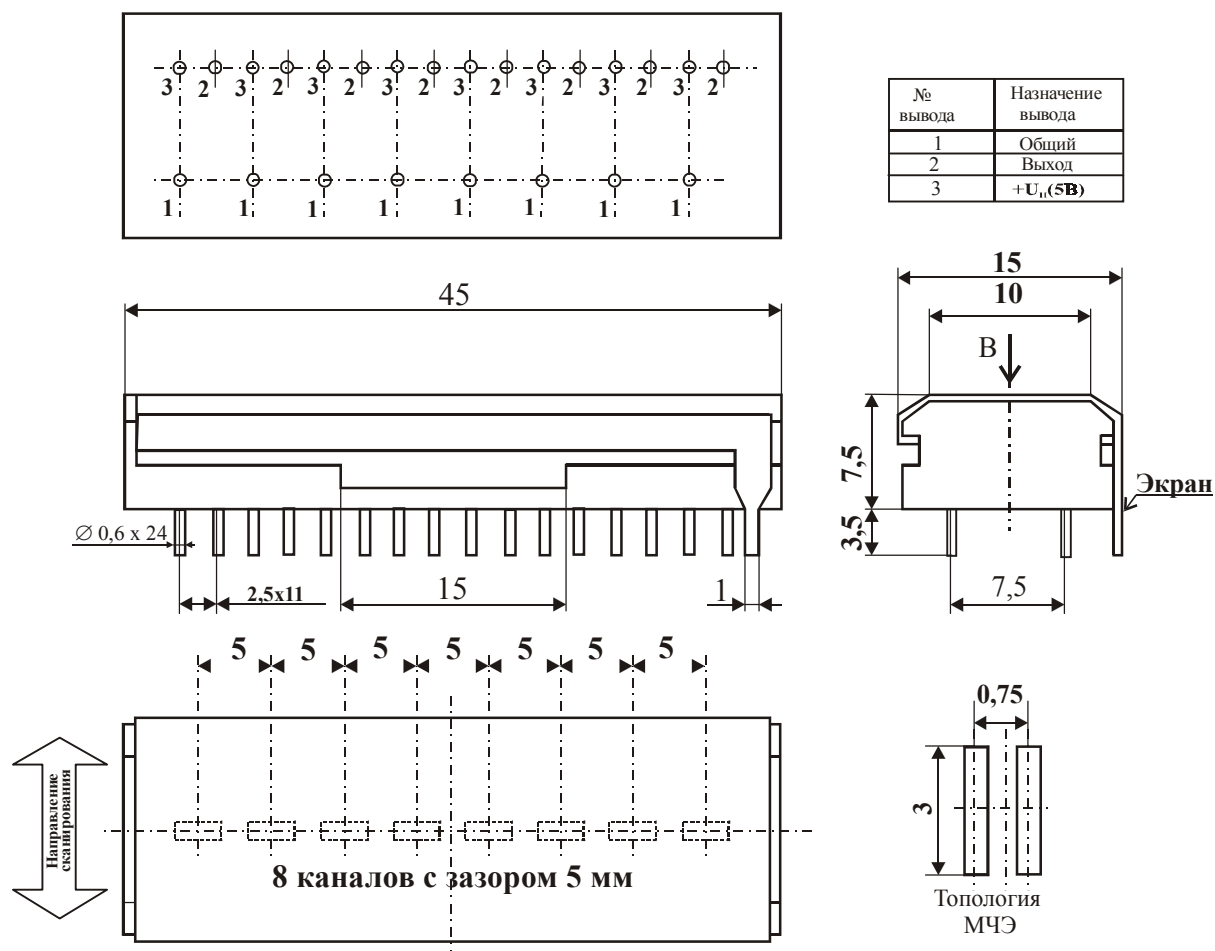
Внешний вид и габаритные размеры датчиков типа BS05M1HFAI
